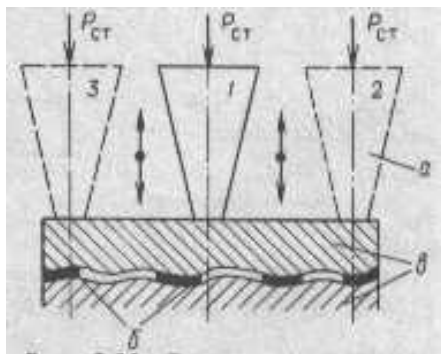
Схема сварки крупногабаритных изделий: а – волновод; б – очаги схватывания; в – свариваемые детали; 1,2,3 – последовательность приложения волновода к изделию
